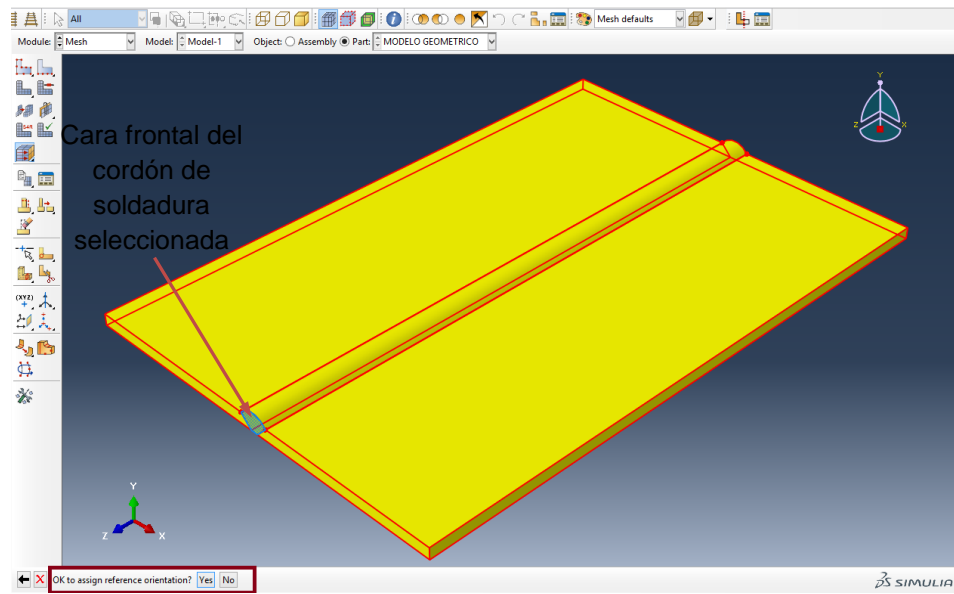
Selección de la cara transversal del cordón de soldadura para realizar apilamiento de elementos de mallado.
